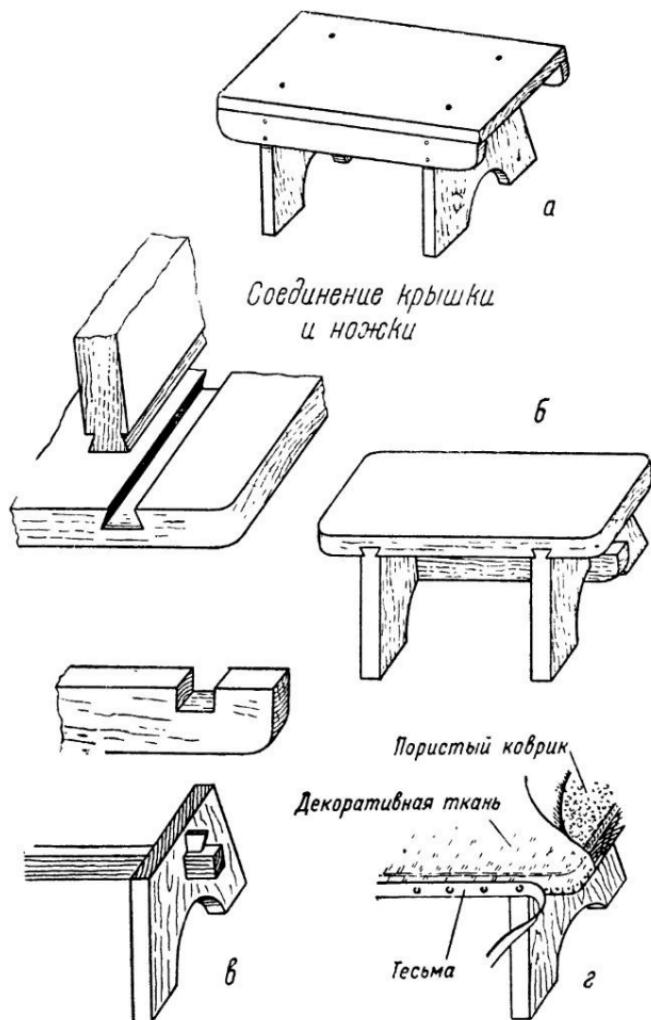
Скамеечки: а — на винтах; б — на клею; в — стяжка ножек шипом с клином; г — прием обивки сидения.
